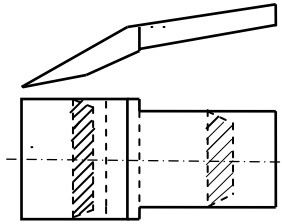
Типичная форма зуба ковша траншейного цепного экскаватора
